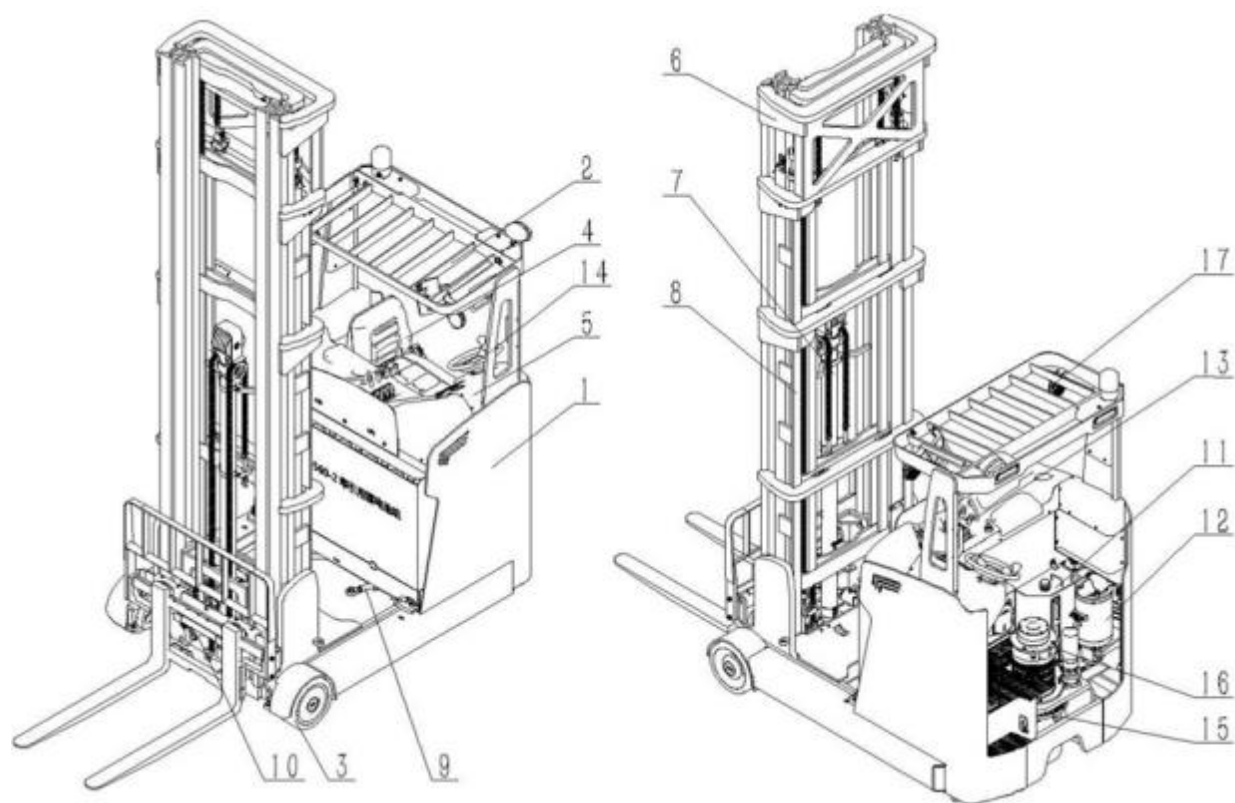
Конструкция ричтрака. Сборочный чертеж:
